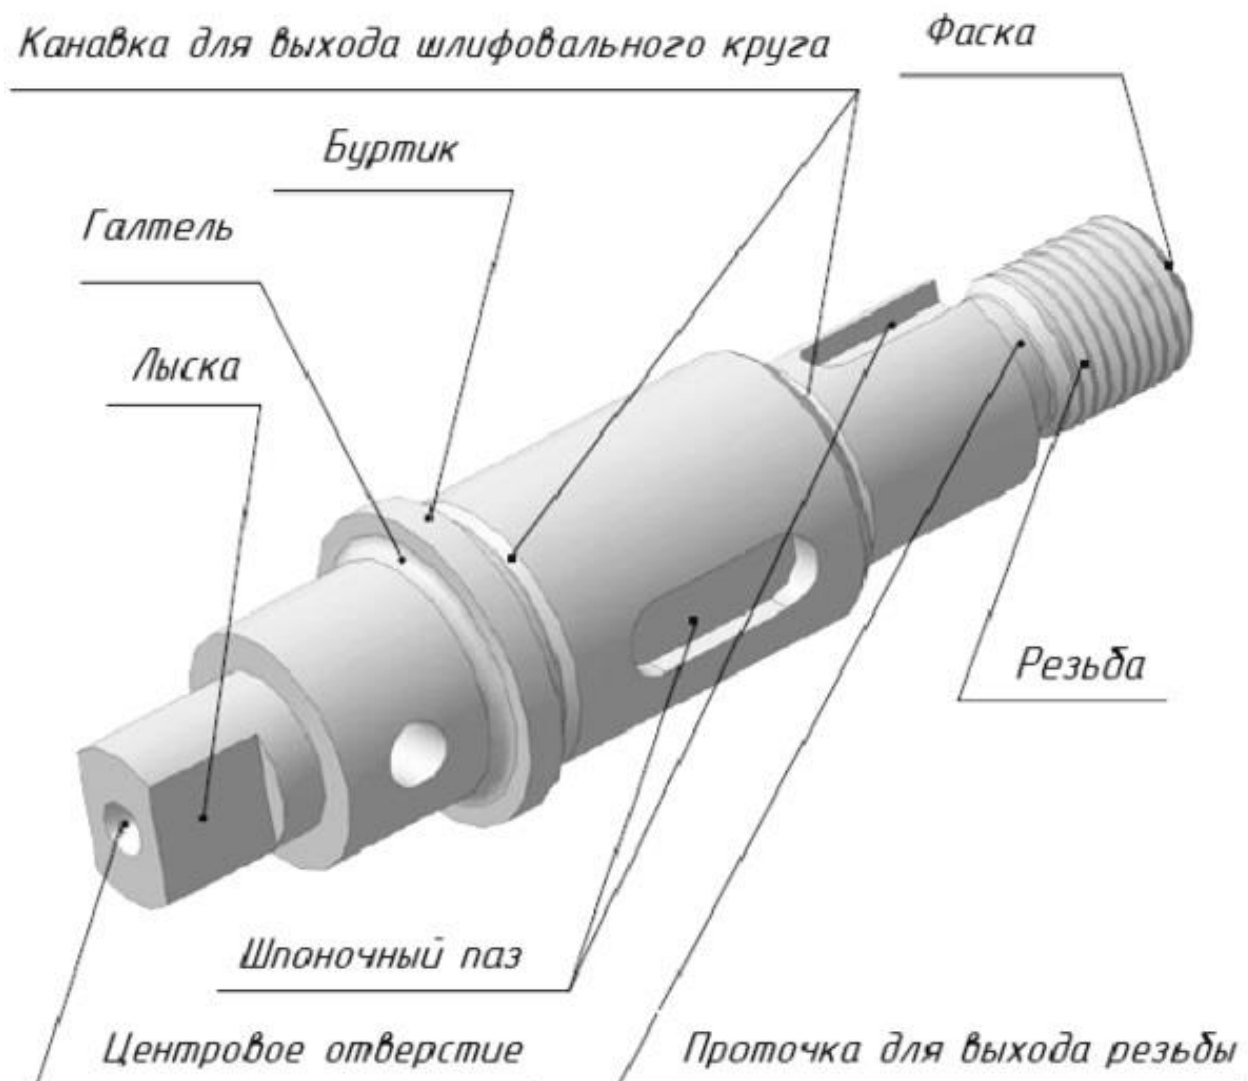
Типовые конструктивные элементы детали типа «вал»
